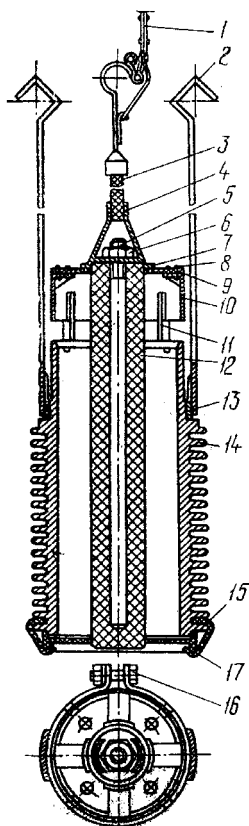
Подвесное приспособление для хромирования цилиндров из алюминиевого сплава:
